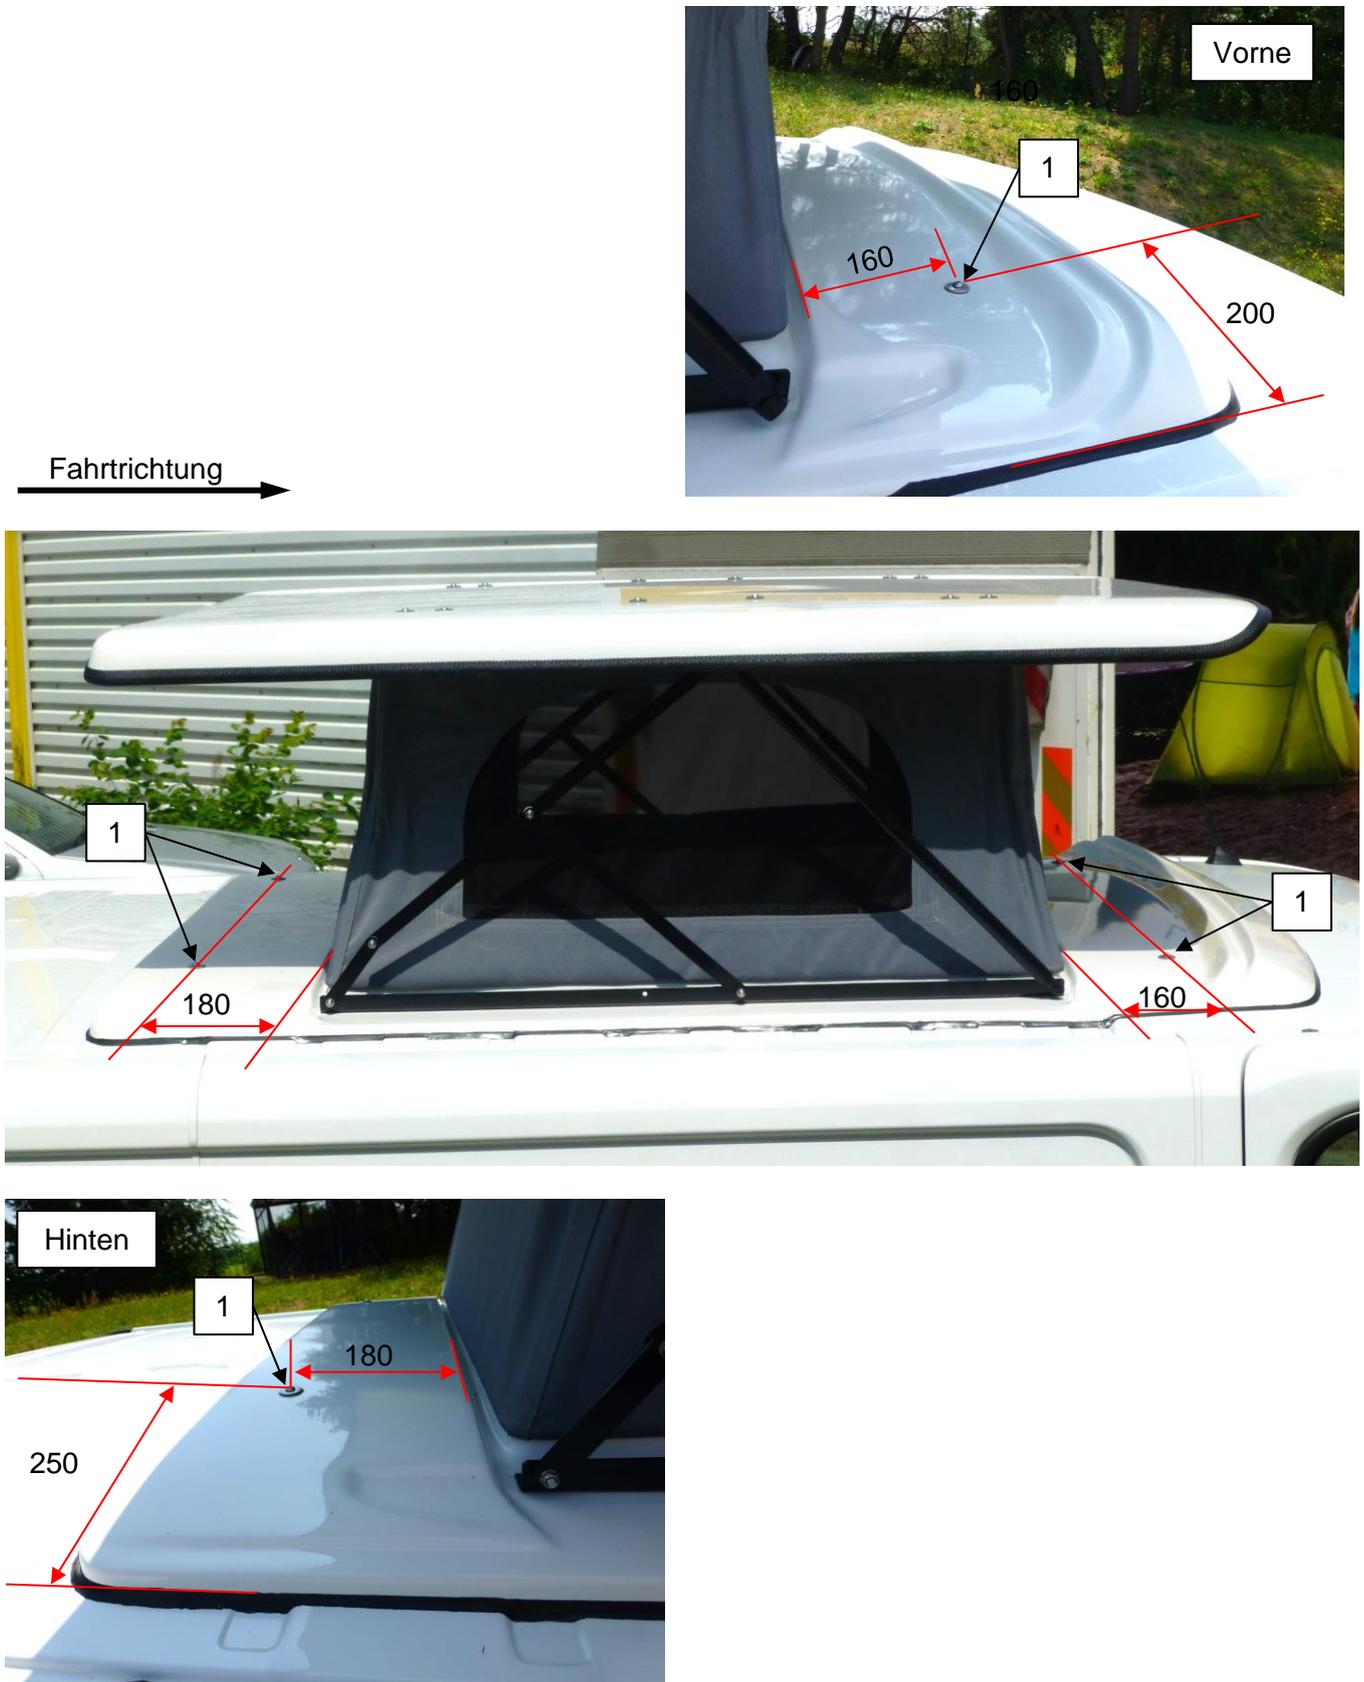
Bohrungen für die Befestigungsschrauben
